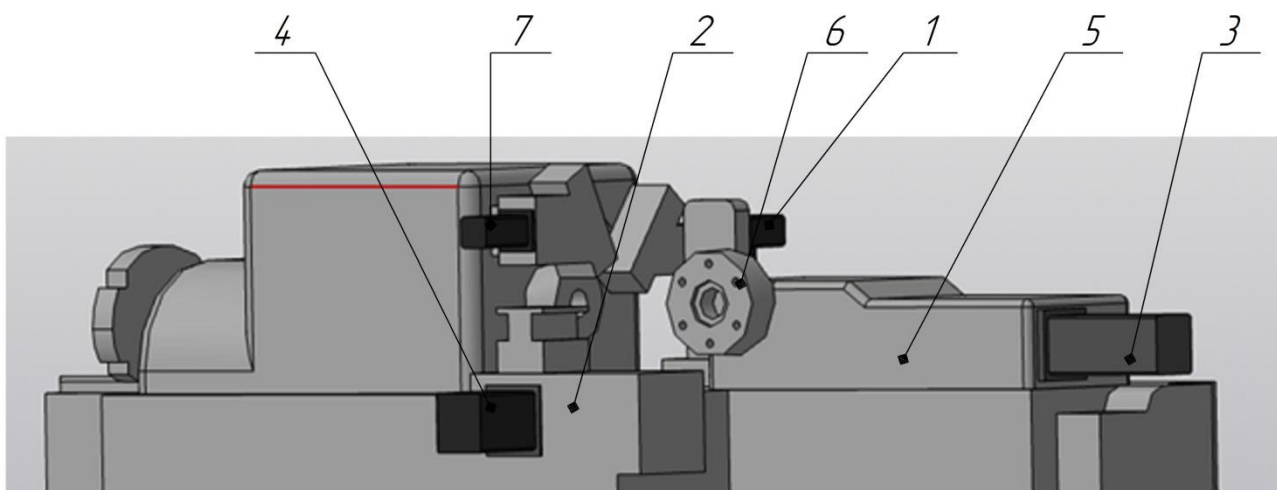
Приводи подач токарно–револьверного верстату автомата 1Б140 після модернізації: 1–двигун позиціонування револьверної голівки; 2–поперечний супорт; 3–серводвигун револьверного супорта; 4–серводвигун поперечного супорта; 5–револьверний супорт; 6–револьверна голівка; 7–серводвигун вертикального супорта.
